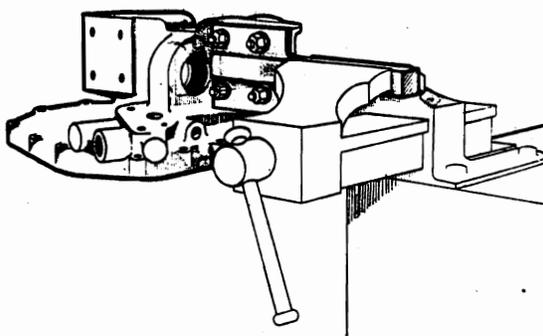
FIXATION DU CARTER ARRIÈRE DANS L'ÉTAU (9° VUE)
